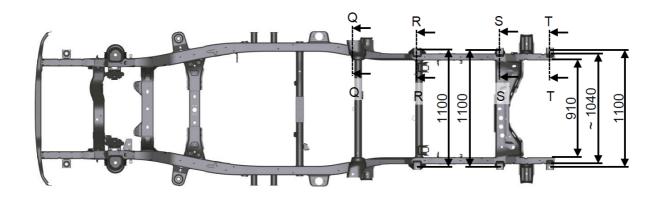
Vista de planta del bastidor tipo escalera Amarok SC
